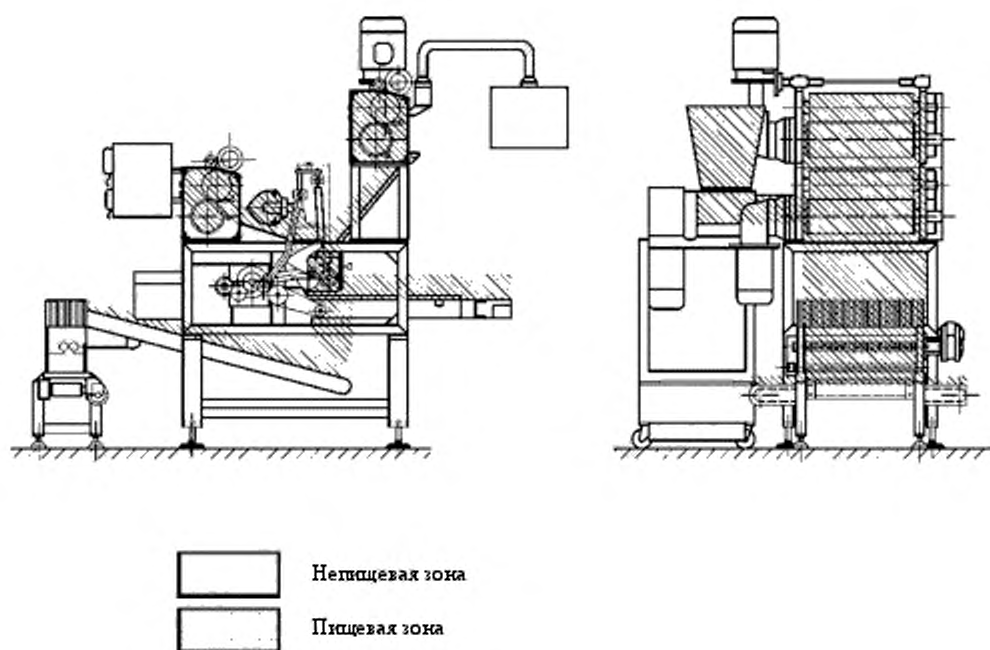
Формовочная машина изделий из теста для обработки двух заготовок из теста
